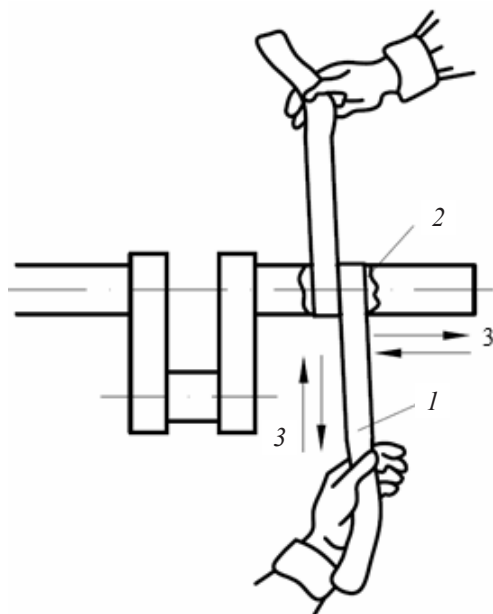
Шліфування шийки вала за допомогою ремня:
